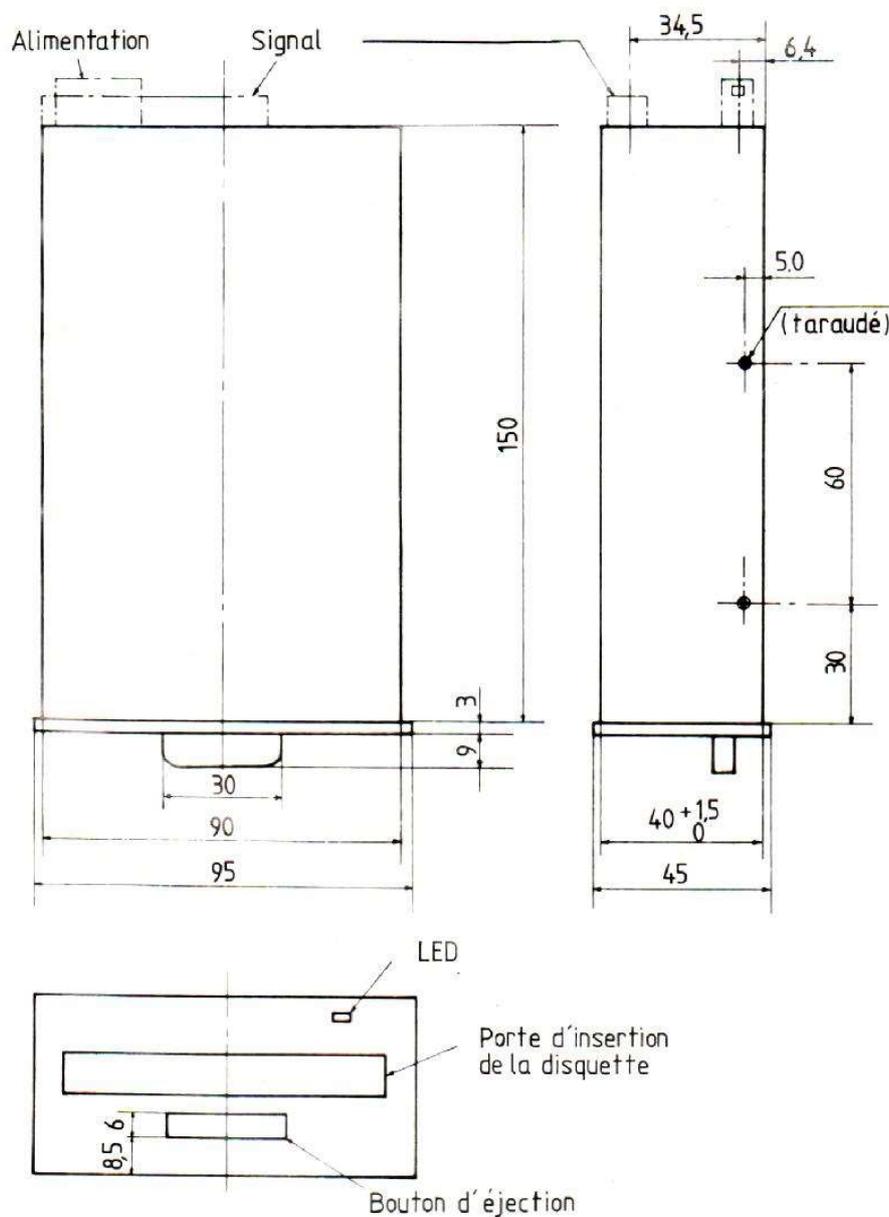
Les dimensions d'un lecteur de microdisquettes.
